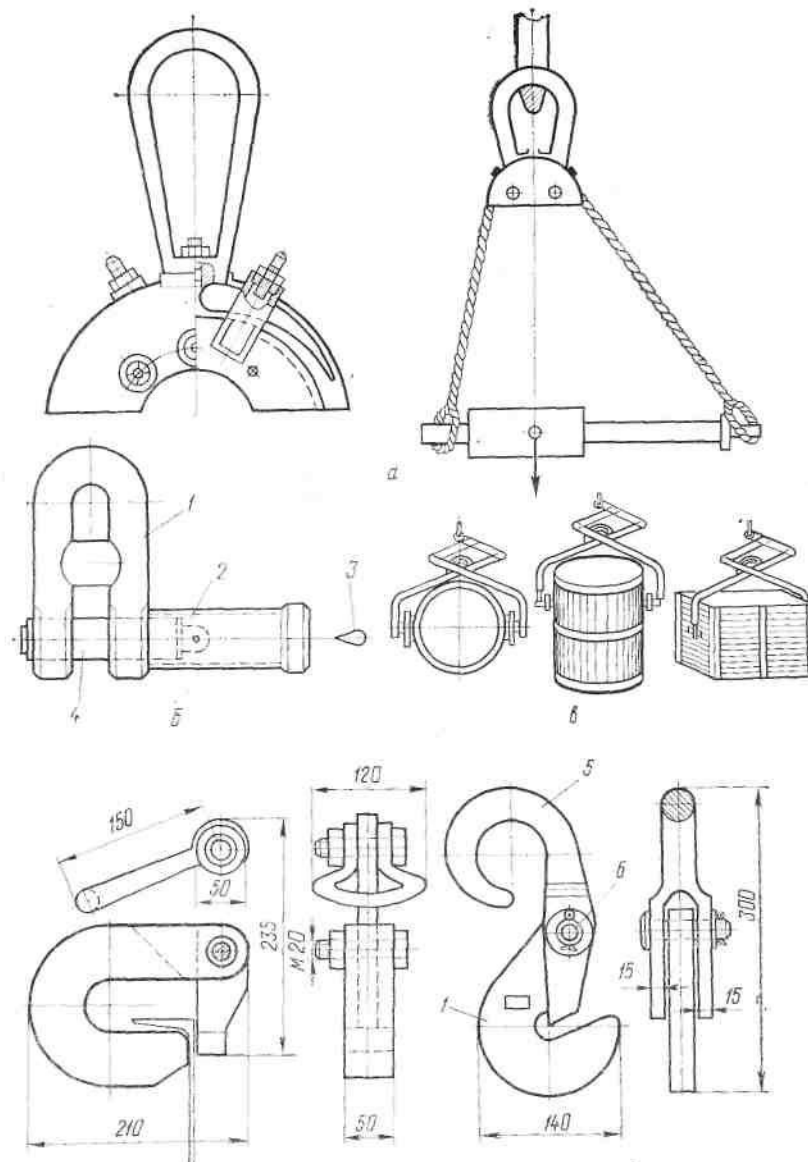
Пристосування для захвату обладнання і елементів металокопрукцій і металопрокату:
